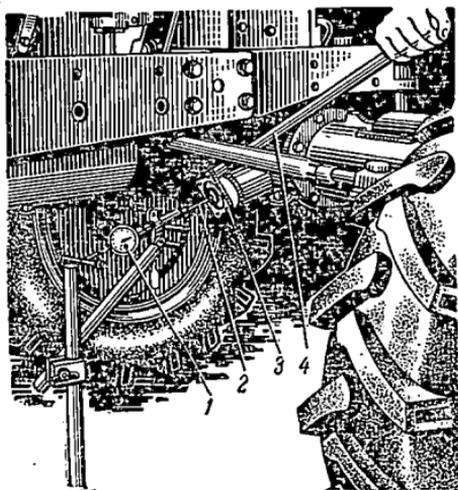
Проверка осевого зазора в подшипниках ведущей шестерни главной передачи трактора МТЗ-52 с помощью приспособления ГОСНИТИ (№ 4270.00.03.000):
